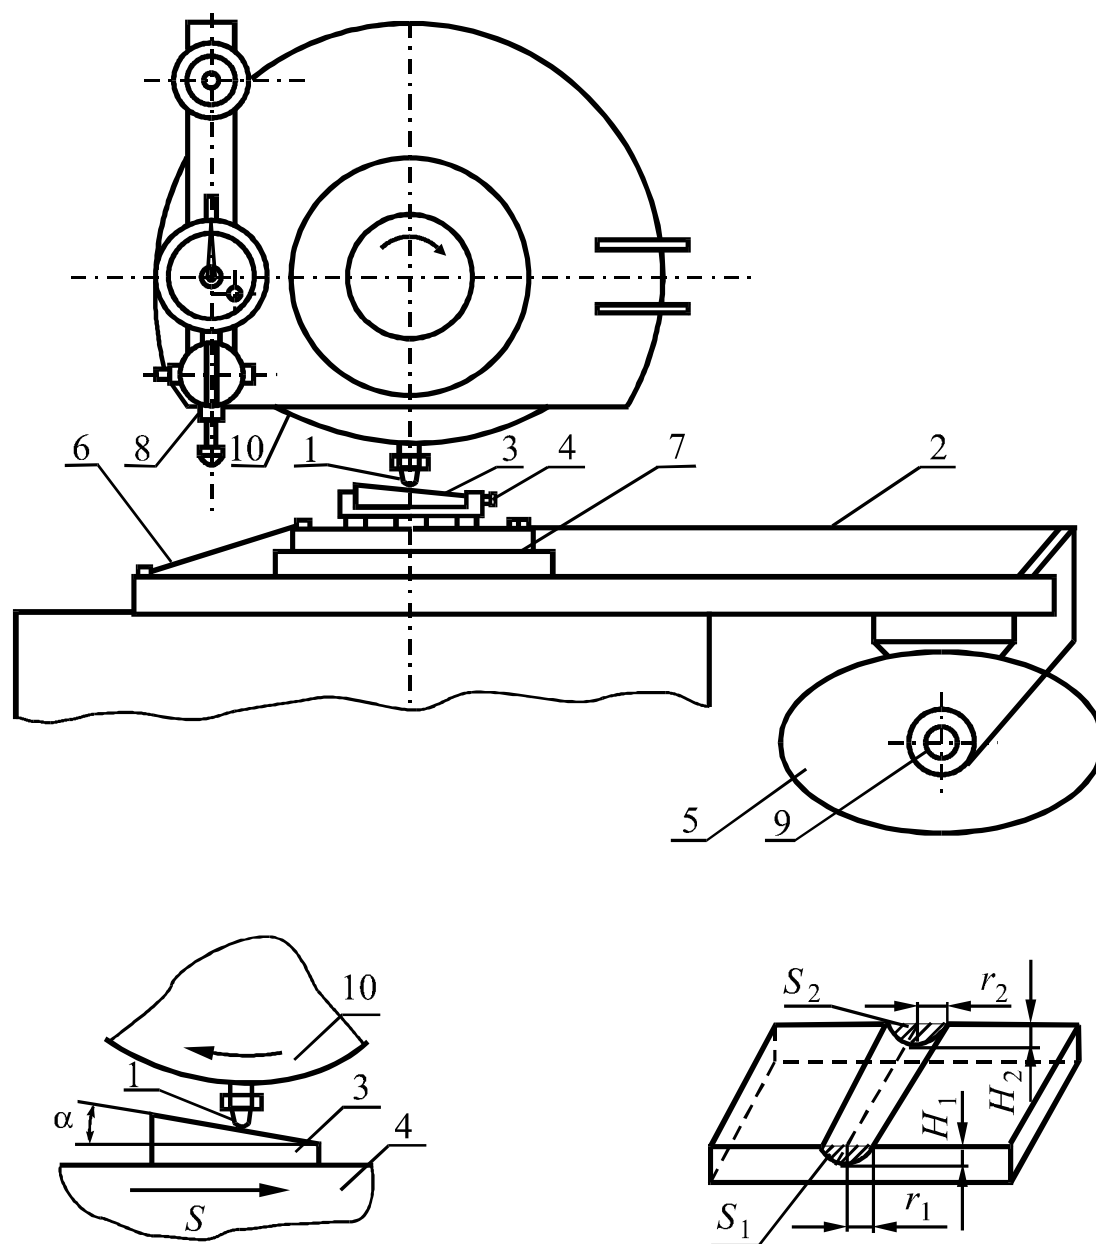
Схема установки для микрорезания на реальных скоростях резания: 1 – оправка с зерном; 2 – стол станка; 3 – образец; 4 – приспособление; 5 – электродвигатель с редуктором; 6 – резиновый жгут; 7 – подвижный столик; 8 – индикатор; 9 – сменные шкивы; 10 – диск; r_1 – радиус дна риска на входе; r_2 – радиус дна риски на выходе; S_1 – сечение среза на входе; S_2 – сечение среза на выходе; H_1 – глубина риски на входе; H_2 – глубина риски на выходе
